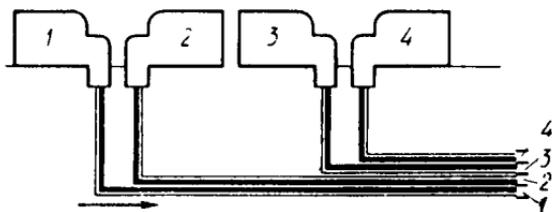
Схема насыпания формирующими машинами трехслойного стружечного ковра:
